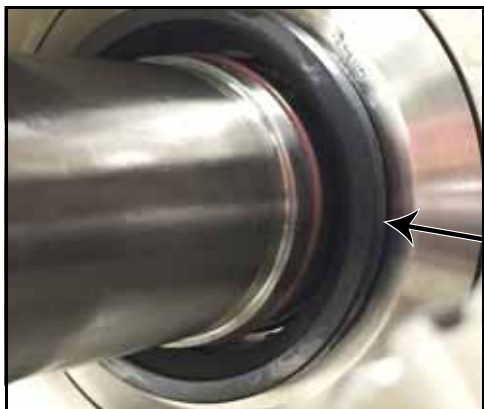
Zdjęcie o-ringa łączącego zaślepkę z wirnikiem
